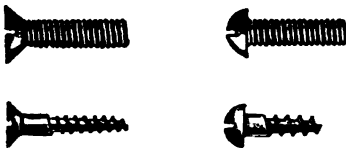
Moderne Schrauben. Oben Metallschrauben, unten Holzschrauben; links flachköpfige, rechts rundköpfige.
